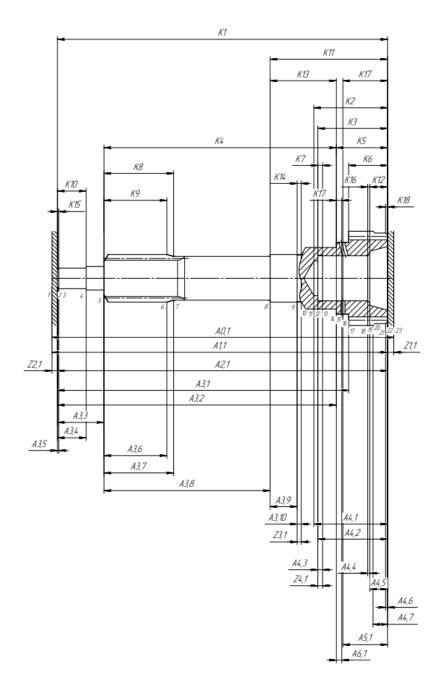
Размерная схема технологического процесса изготовления «ведущий вал коробки передач»
